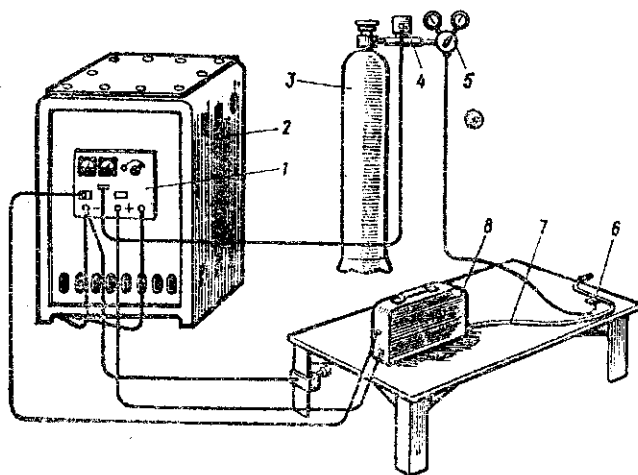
Схема поста полуавтоматической сварки в среде углекислого газа:
